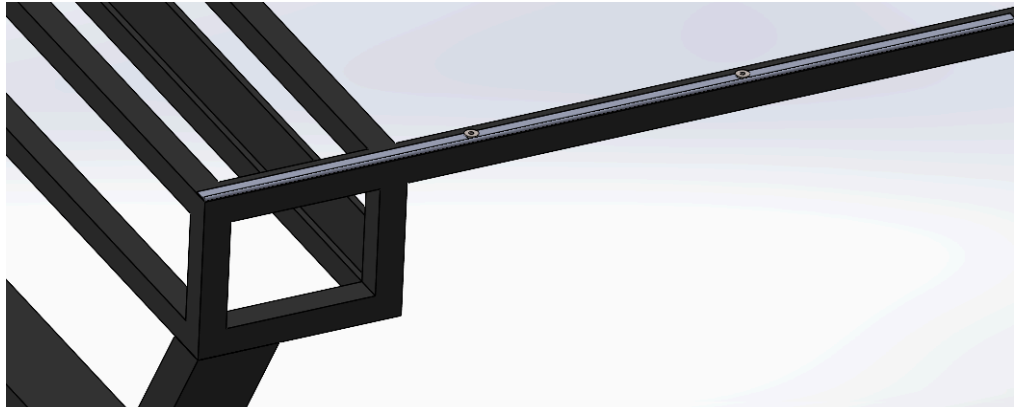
Detalle Bisagra de Piano (Fuente: Elaboración propia)
